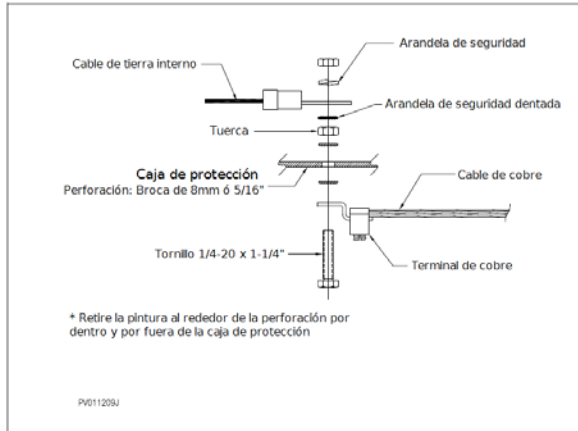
Fijación de los cables de aterrizamiento a la caja de protección.
